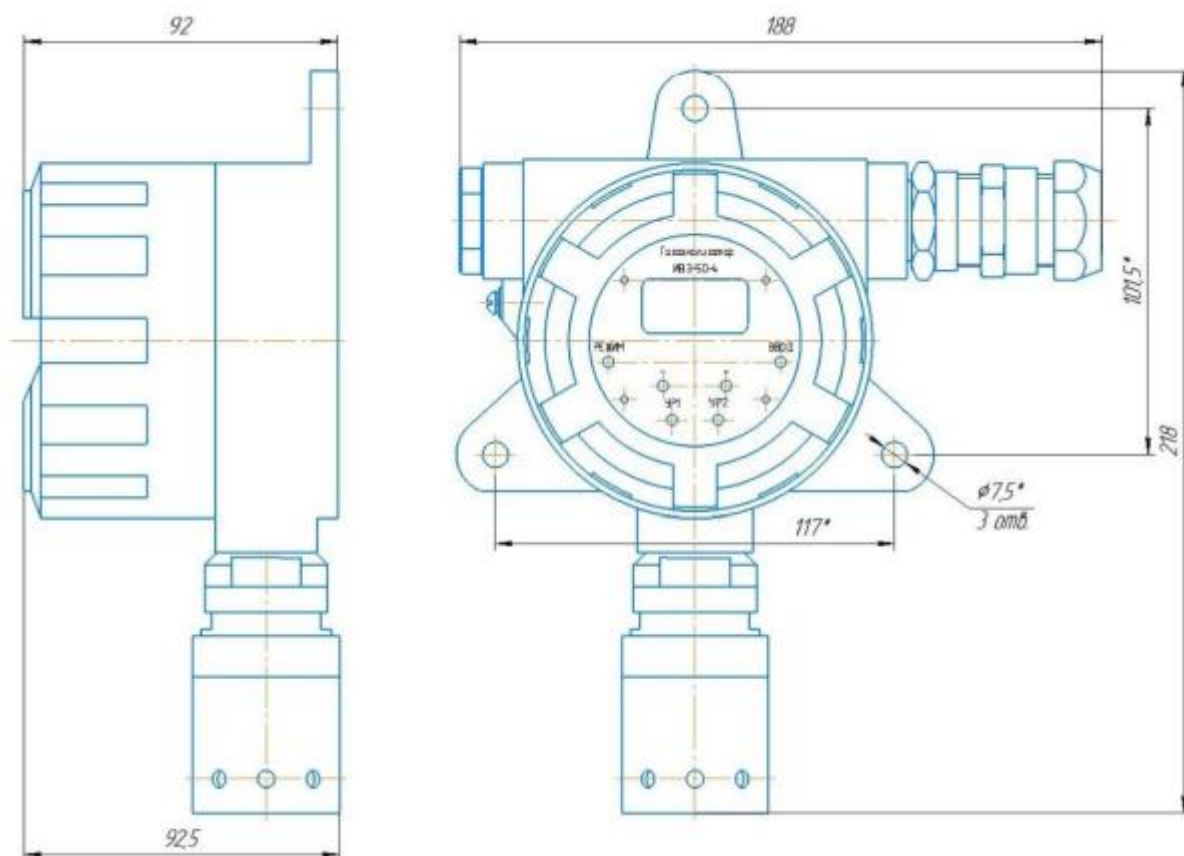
Габаритные размеры ИВЭ-50-4 (корпус обычный)
